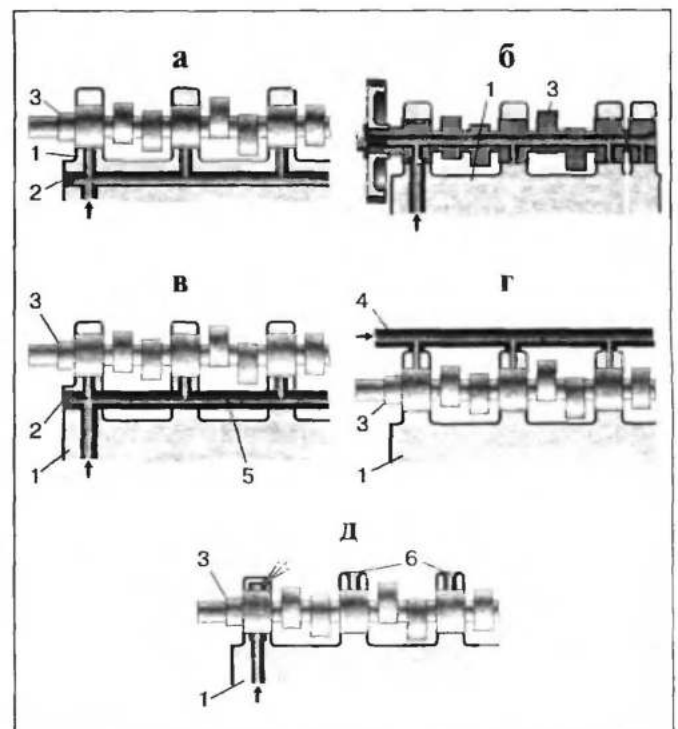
Основные схемы подачи масла к подшипникам распределительных валов: а — подводом масла через каналы к каждой опоре; б — через полый распределительный вал; в — через ось коромысел; г — через маслоподающие трубки; д — комбинированная система смазки (часть опор имеет маслоборные отверстия, куда масло поступает после разбрызгивания); 1 — головка блока (блок); 2 — заглушка; 3 — распределительный вал; 4 — трубка; 5 — ось коромысел; 6 — маслоборные отверстия
